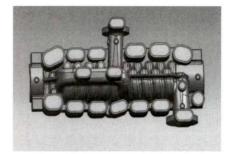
泵体铸件冒口和补贴布置图 Fig.2 Risers and pads layout of the pump casting
